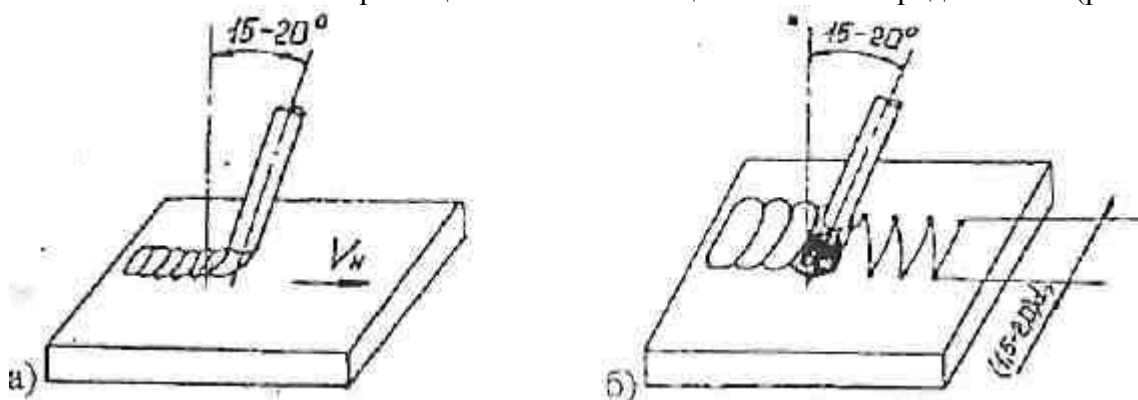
Схема наложения узких (а) и широких (б) валиков при ручной дуговой наплавке покрытыми электродами
